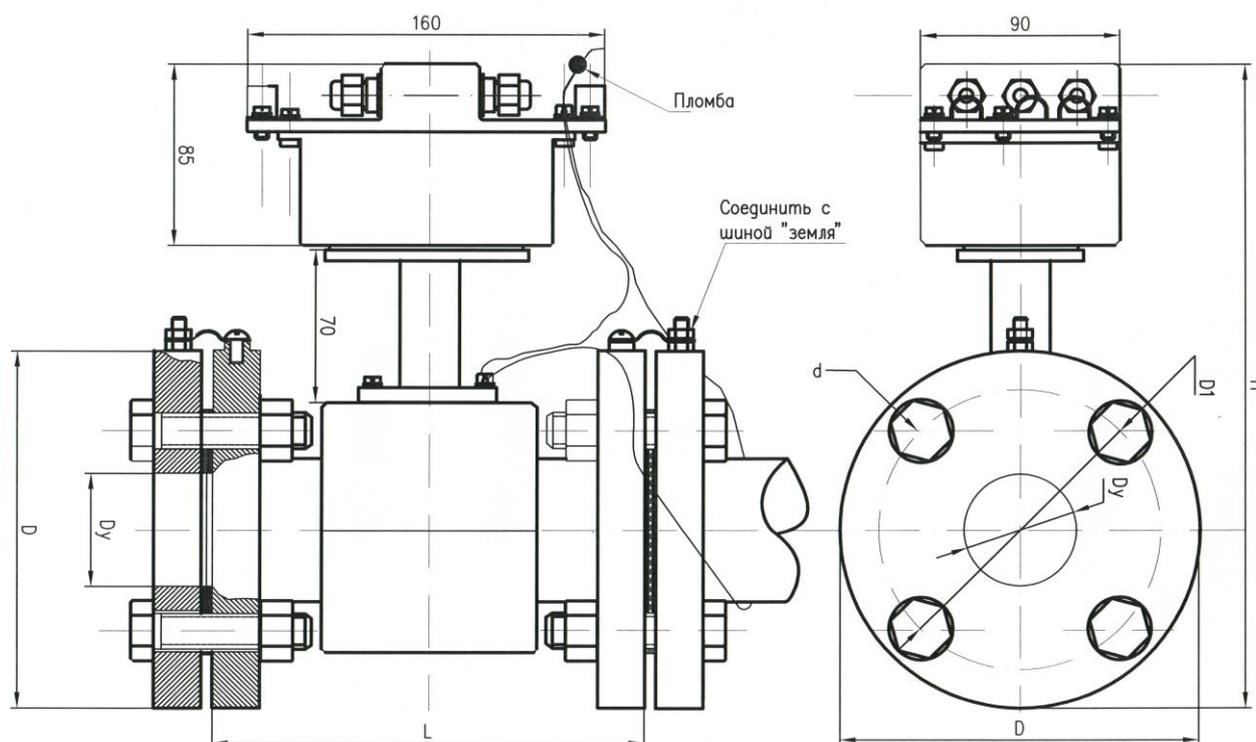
Габаритный чертеж и схема пломбирования ИБ.
